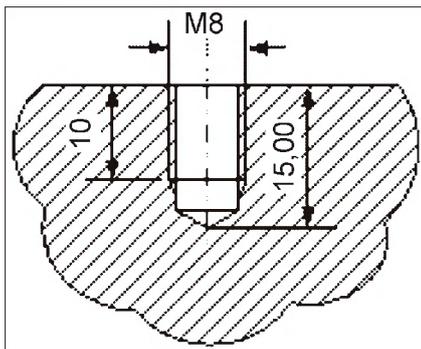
Резьбовое отверстие для крепления датчика температуры на подшипниковых узлах лебедок, двигателей и корпусах приводных двигателей и генераторов
